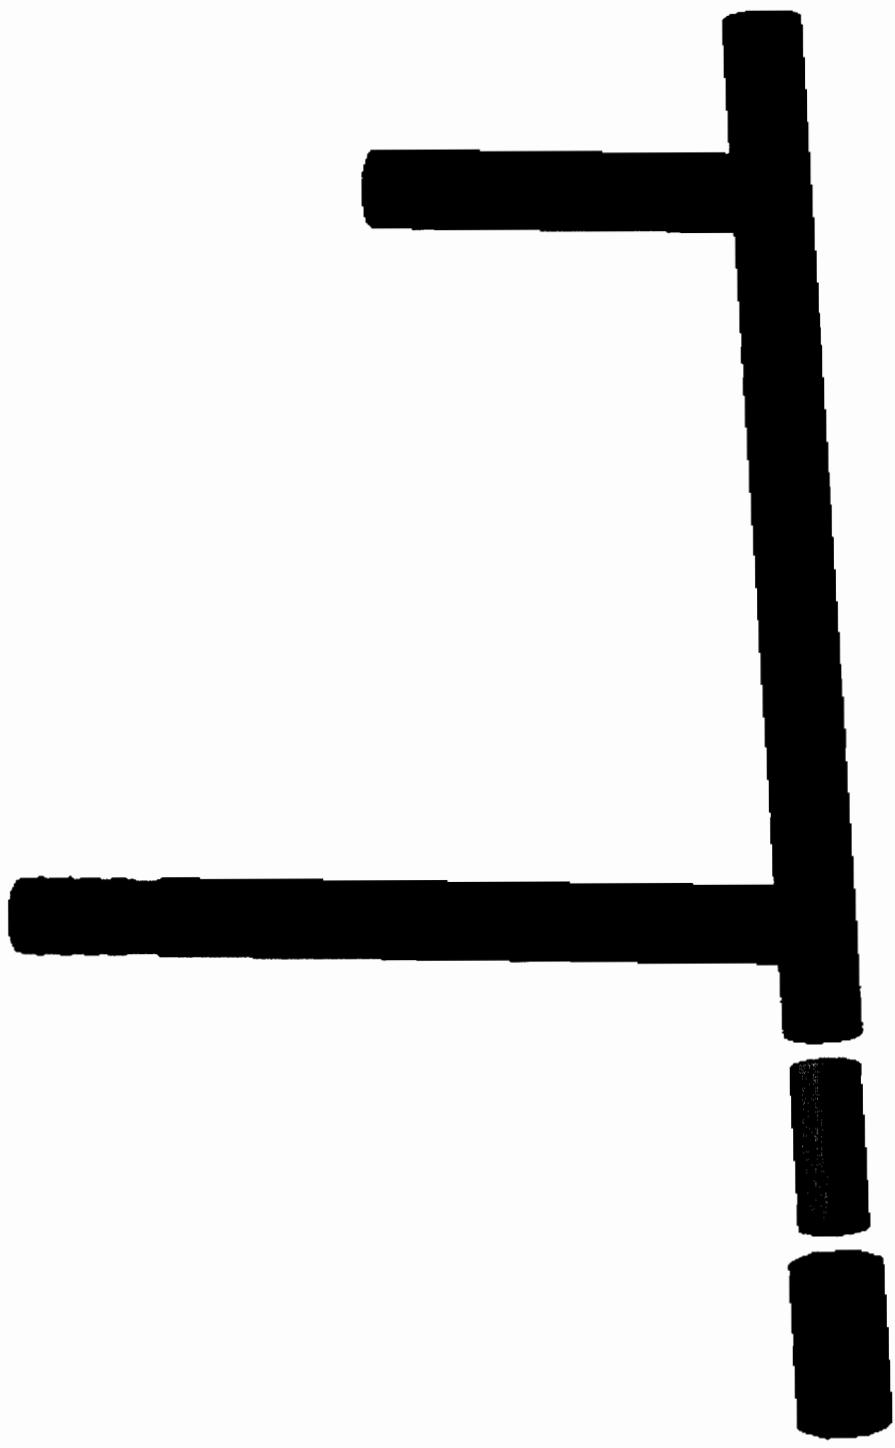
Vedere de ansamblu (in manieră explodată) a detaliului
